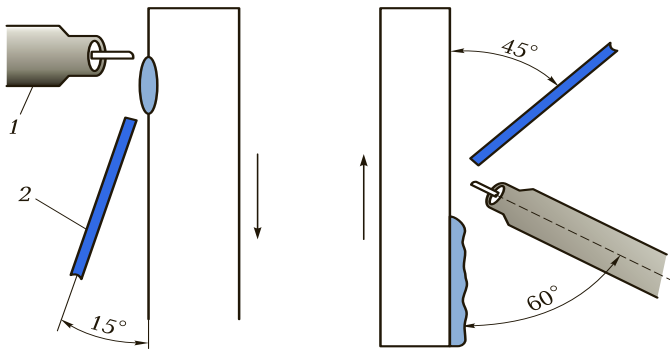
Положение горелки 1 и присадочной проволоки 2 при сварке в вертикальном положении
